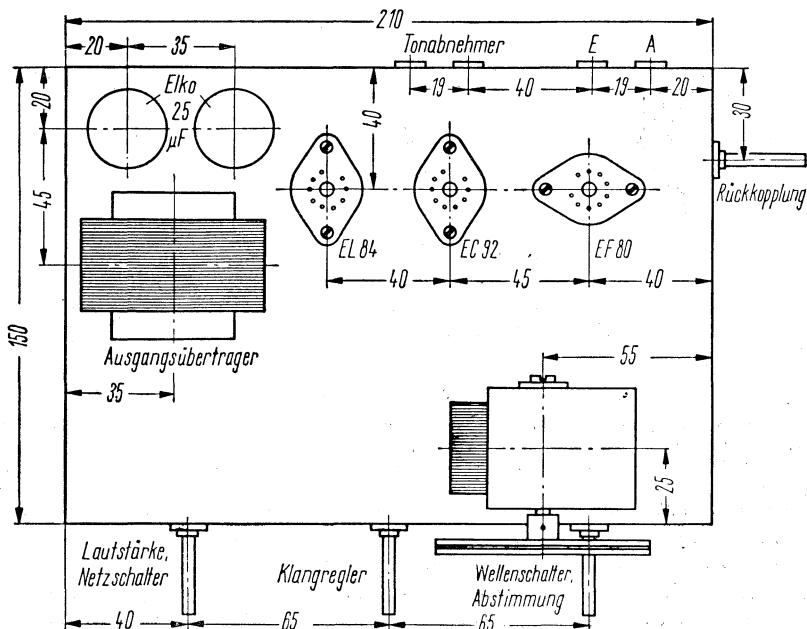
Aufbauplan eines einfachen Einkreis-Empfängers
